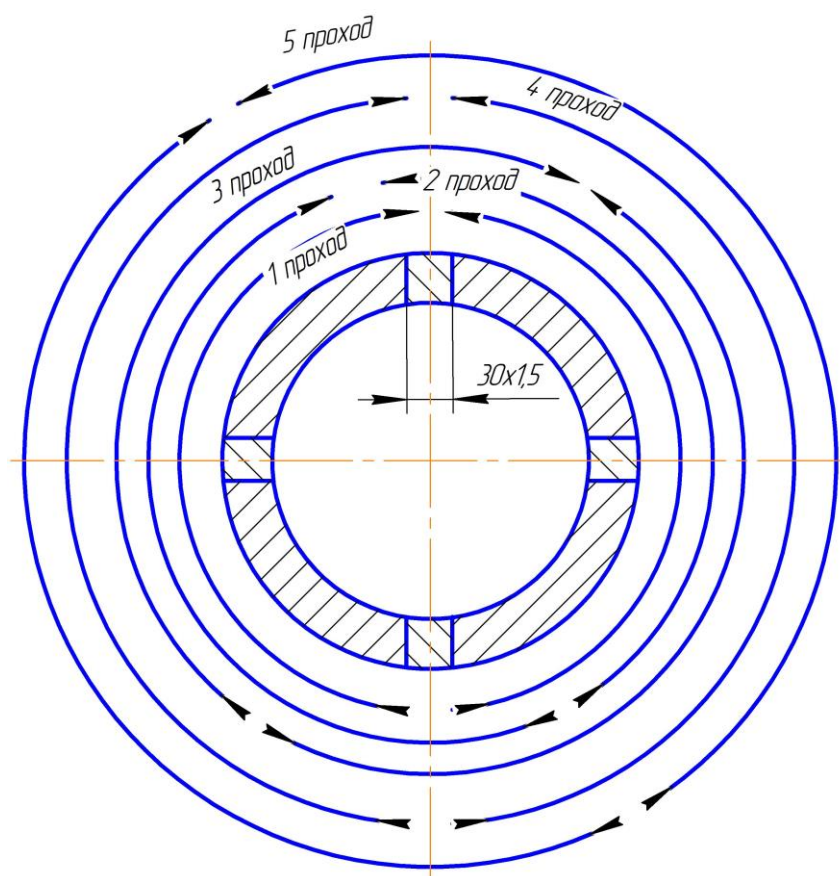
Схема расстановок прихваток, порядок выполнения швов.
